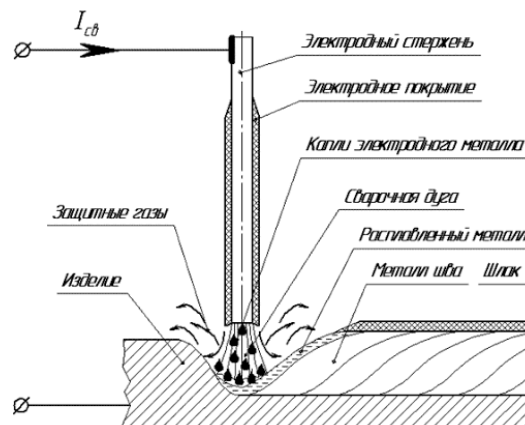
Схема сварки покрытыми электродами
